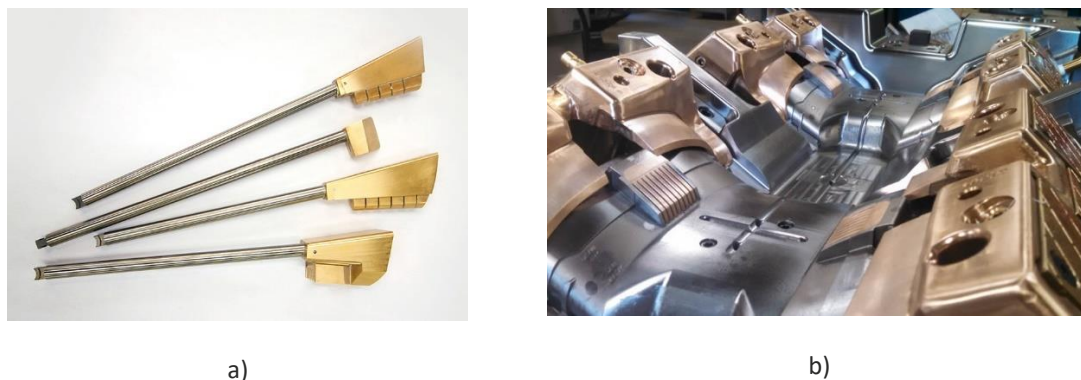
Utilização do AMPCOLOY® 83: a) Inserto de extração (adaptado de [93]); b) Molde de injeção (adaptado de [94])
